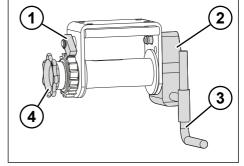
Zurrgurtwinde mit Aufsteckgetriebe
